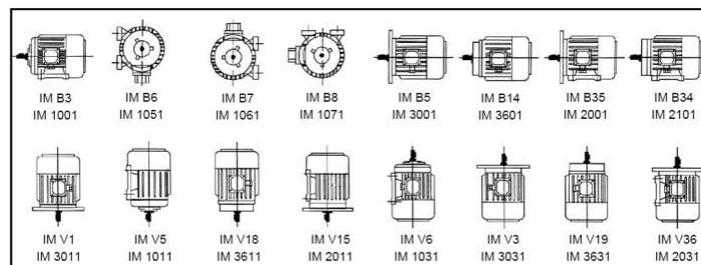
Forma constructiva posición de montaje según norma IEC34-7
